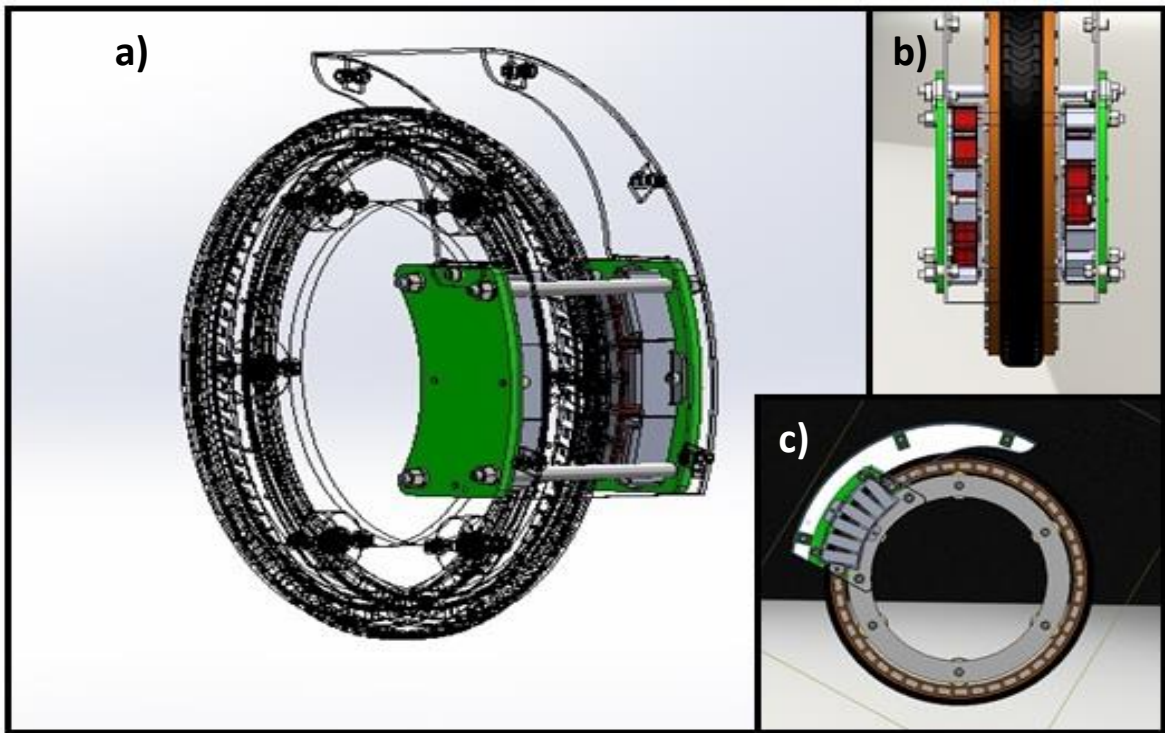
Vistas del Subensamble del Soporte Tipo Caliper. a) vista isométrica, b) vista frontal y c) vista lateral.
